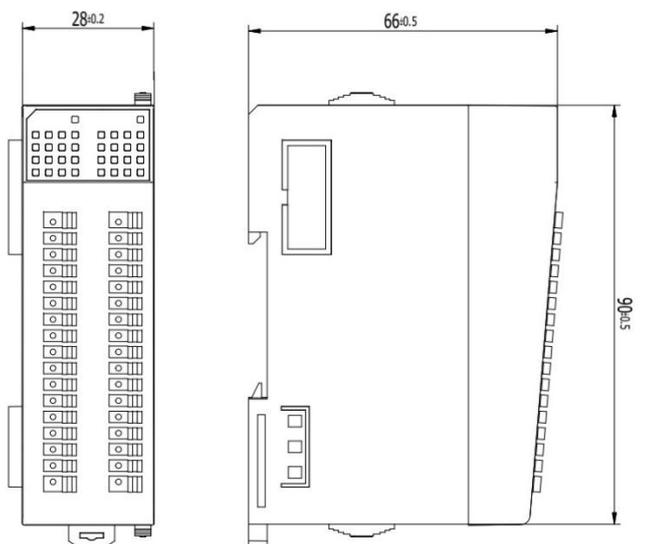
Габаритные размеры для SM213S18, SM313S19.
